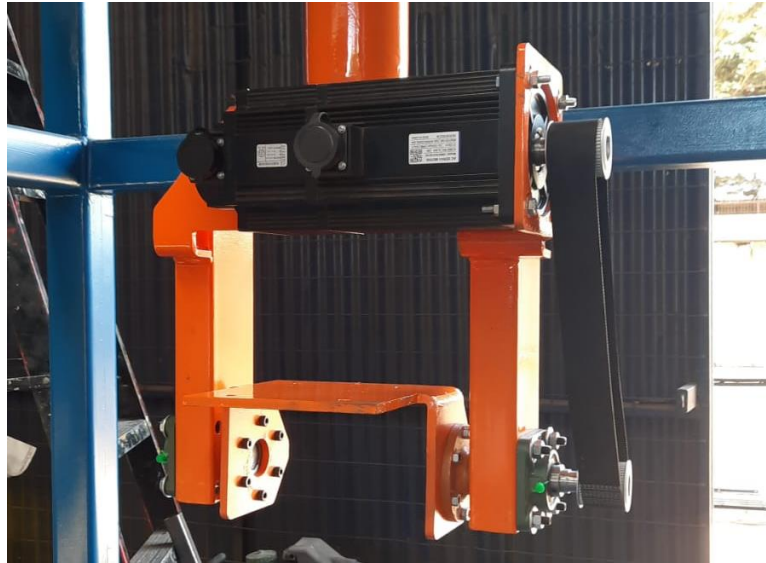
Montaje de transmisión para movimiento rotacional en Eje X.
